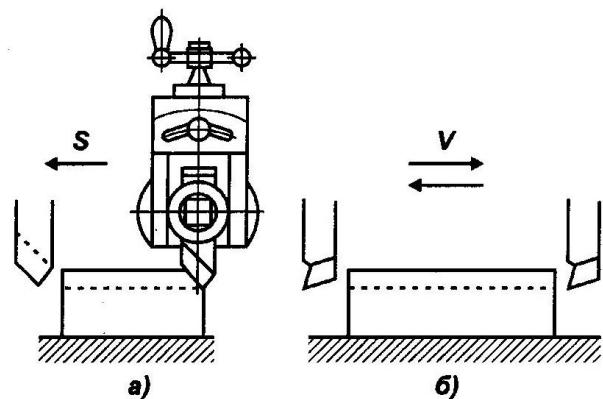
Схеми обробки поверхонь струганням:
